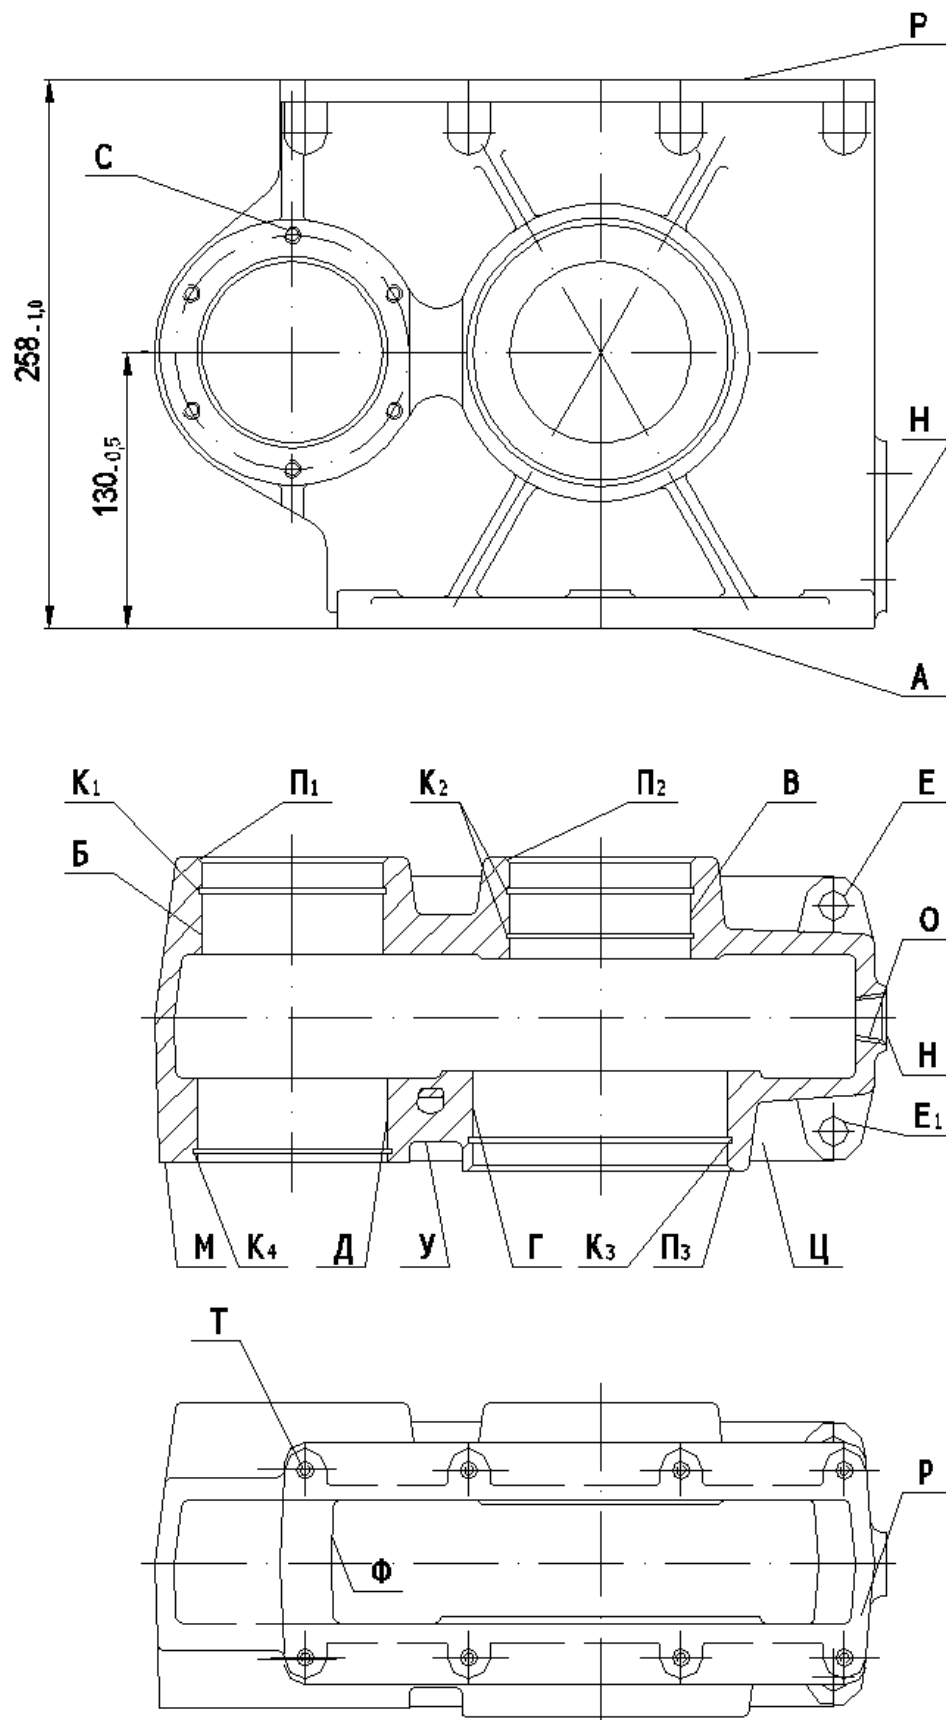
Позначення поверхонь корпусу КС6В-48.101
